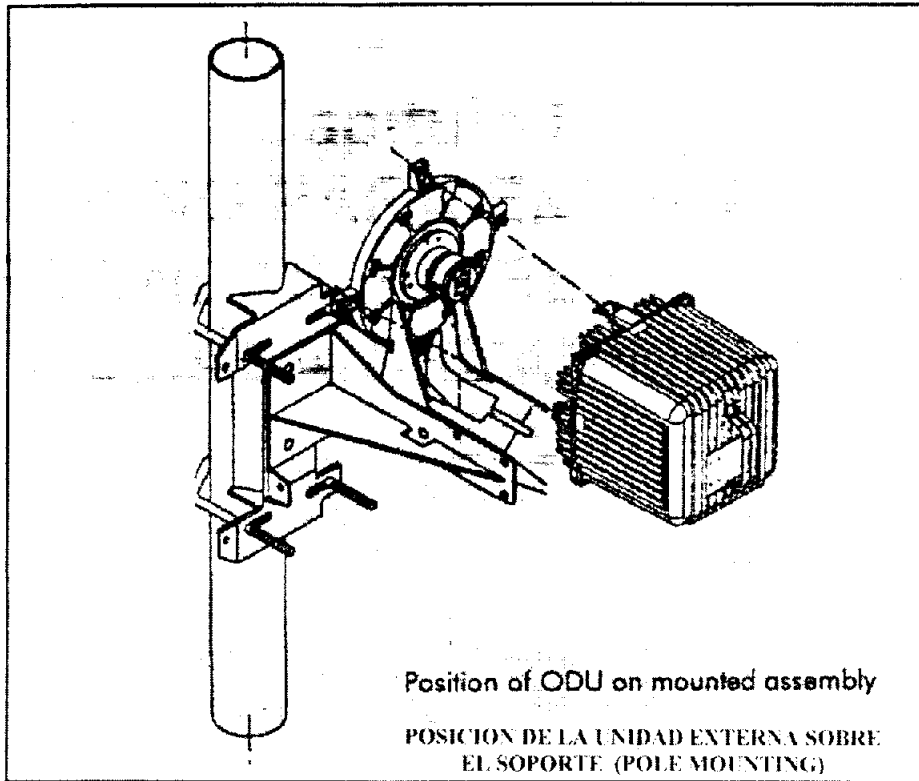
e) - Instalación del equipo de radio sobre el pole mounting (soporte)
